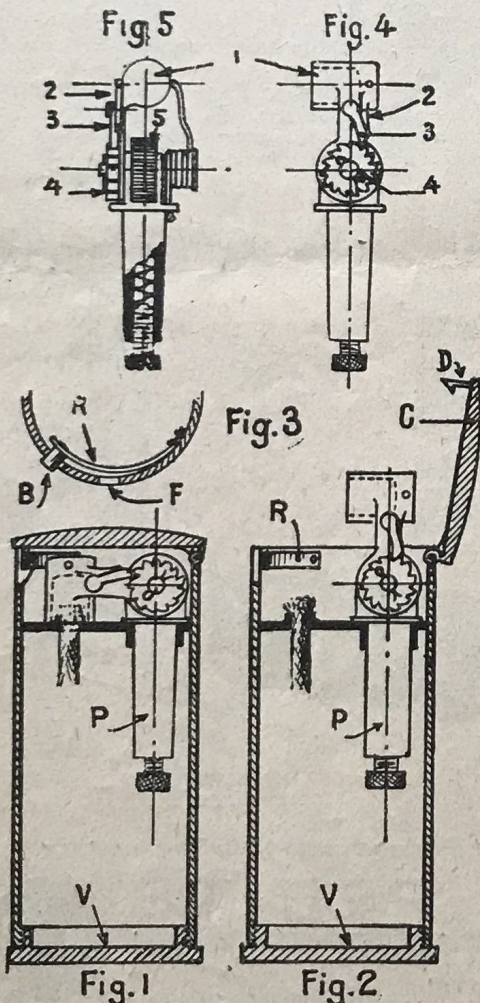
ET 2. — Vues en coupe du briquet avant et après le fonctionnement. — FIG. 3. Vue du bouton de déclenchement. — FIG. 4 ET 5. Détail agrandi du porte-pierre et du porte-molette.
